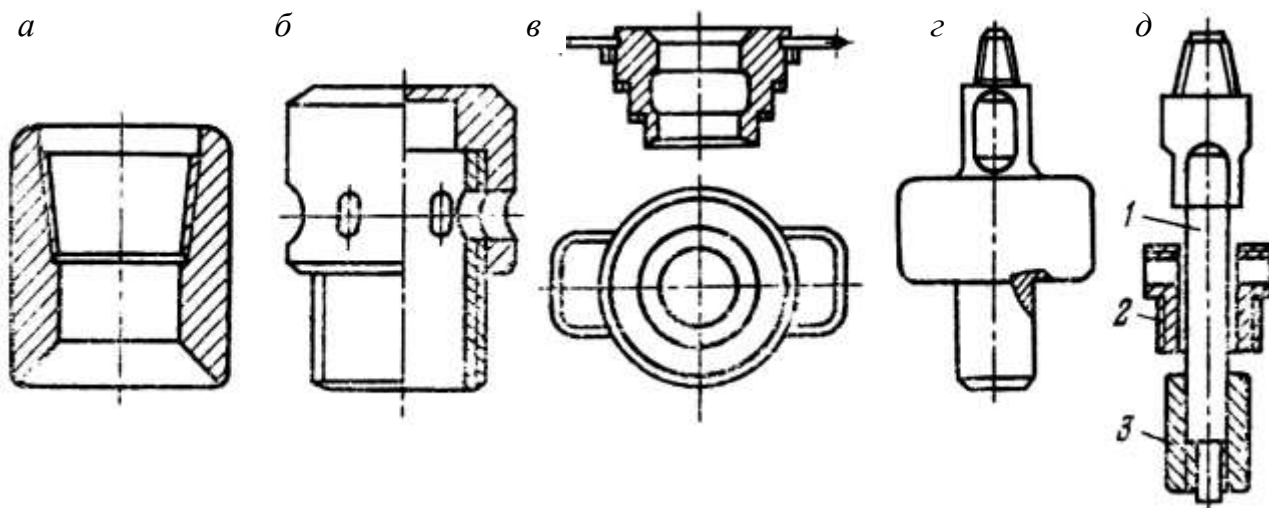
Допоміжний інструмент для обсадних труб:
